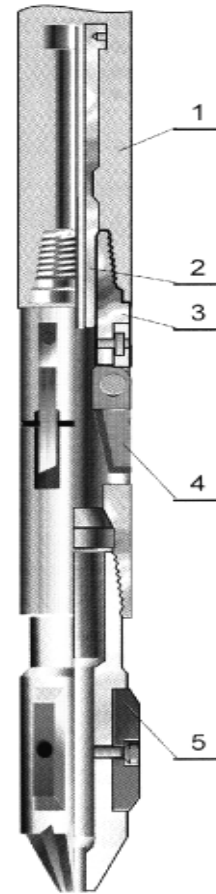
Расширитель раздвижной типа РР.000: 1 – корпус вырезающего устройства; 2 – толкатель; 3 – корпус расширителя; 4 – лопасть; 5 – центратор
